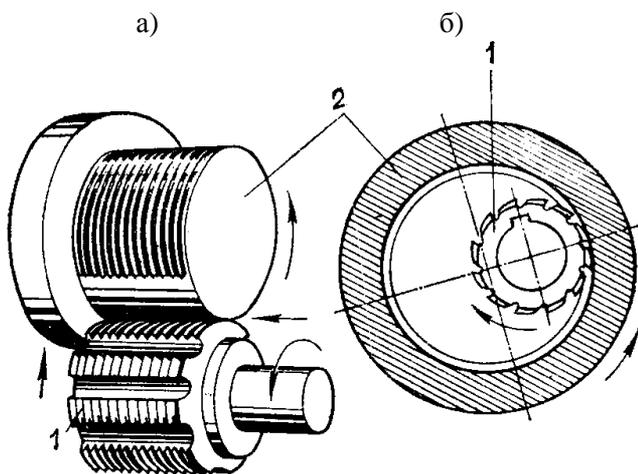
Схема работы гребенчатых резьбовых фрез при нарезании наружной (а) и внутренней (б) резьбы
